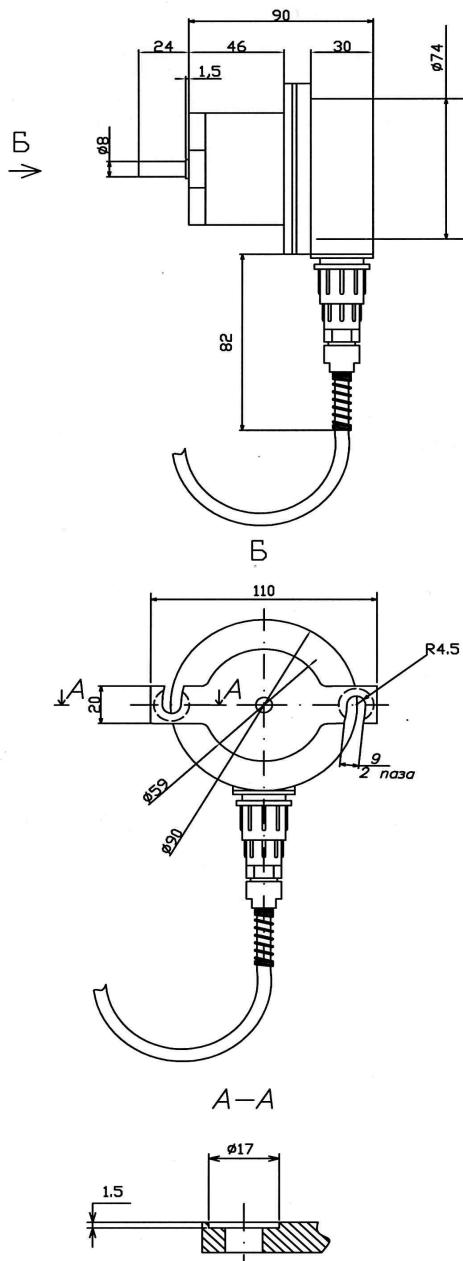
Габаритные и присоединительные размеры ДГИ
